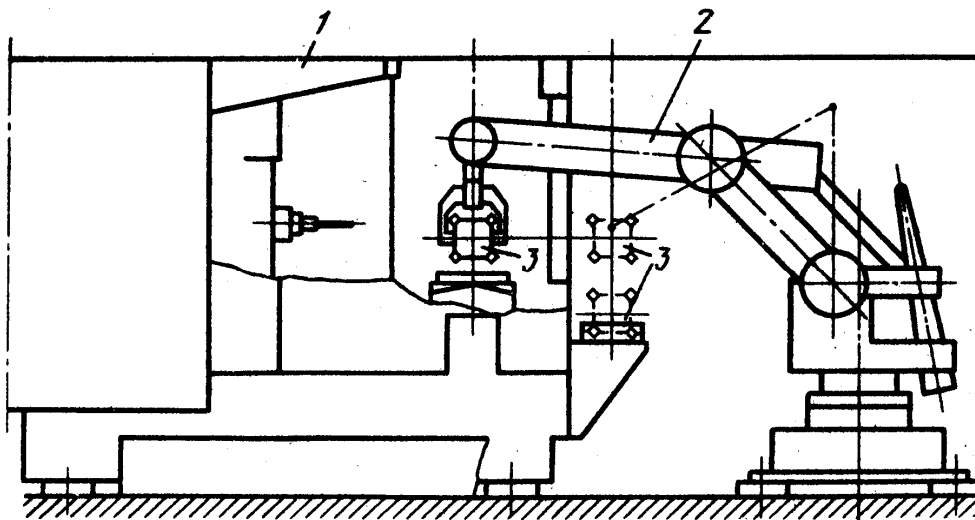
Універсальний робот у ГРТК для оброблення призматичних деталей
